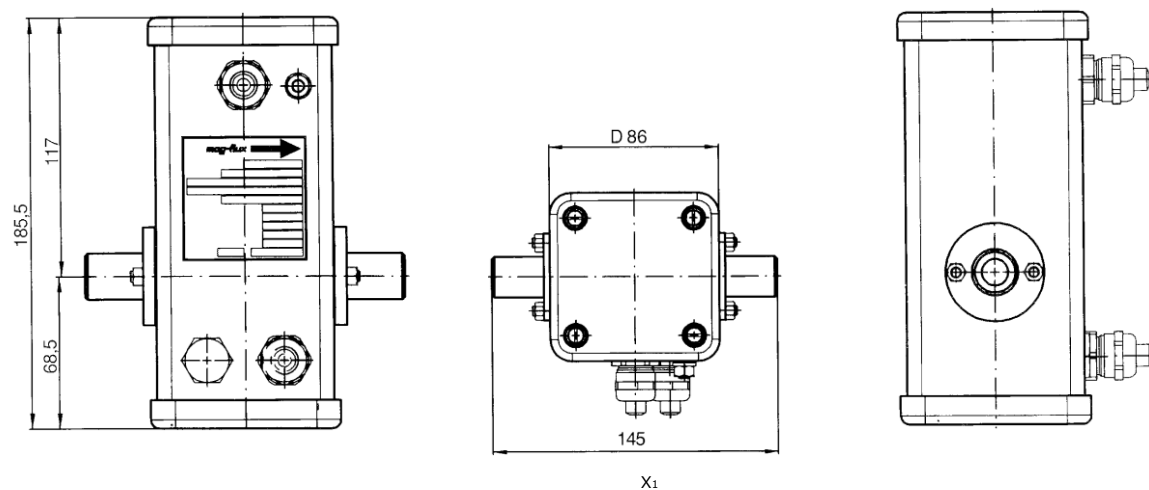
Sensore di flusso magnetico F5 (senza montaggio a parete), dimensioni in mm
